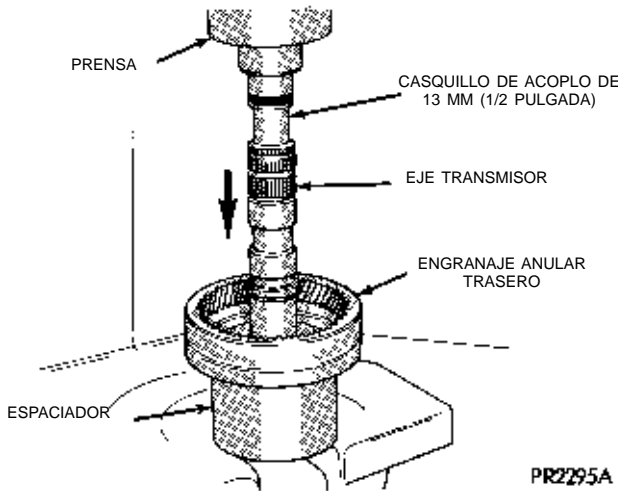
Instalación del cono de cojinete del engranaje del eje transmisor
